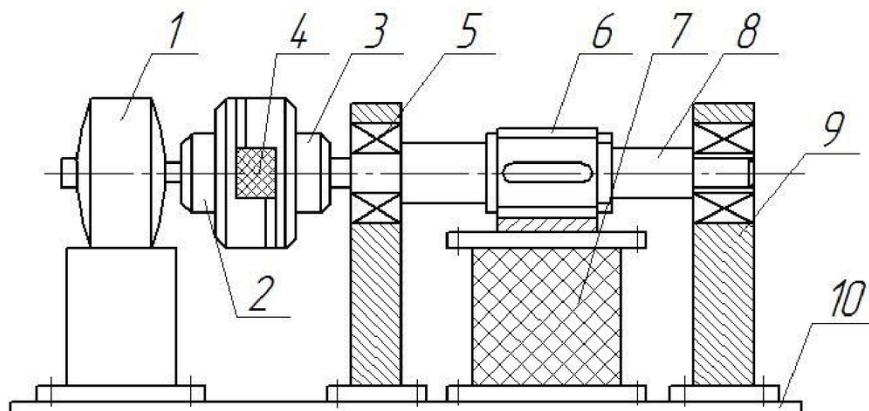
Кинематическая схема испытательного стенда: 1 - электродвигатель; 2,3 - полумуфты; 4 - упругий элемент; 5 - подшипник; 6 - кулачок; 7 - амортизатор; 8 - вал; 9 - корпус подшипника; 10 - основание.
